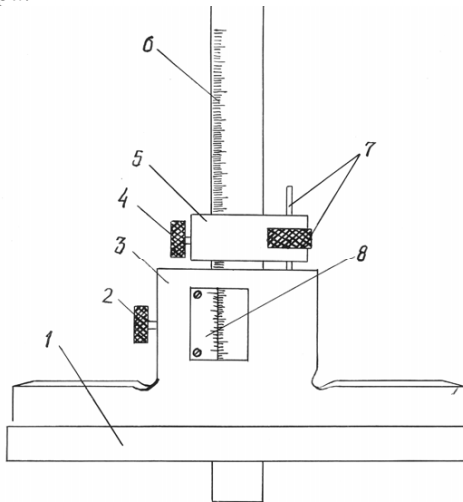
Штангенглибиномір: 1 – основа; 2 – затискач рамки; 3 – рамка; 4 – затискач рамки мікрометричної подачі; 5 – рамка мікрометричної подачі; 6 – штанга; 7 – гайка і гвинт мікрометричної подачі; 8 – ноніус
